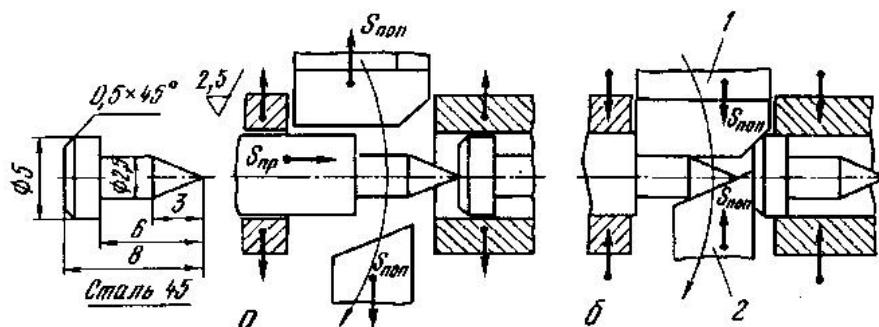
Схема обробки заготовки на фасонно-відрізному автоматі:
